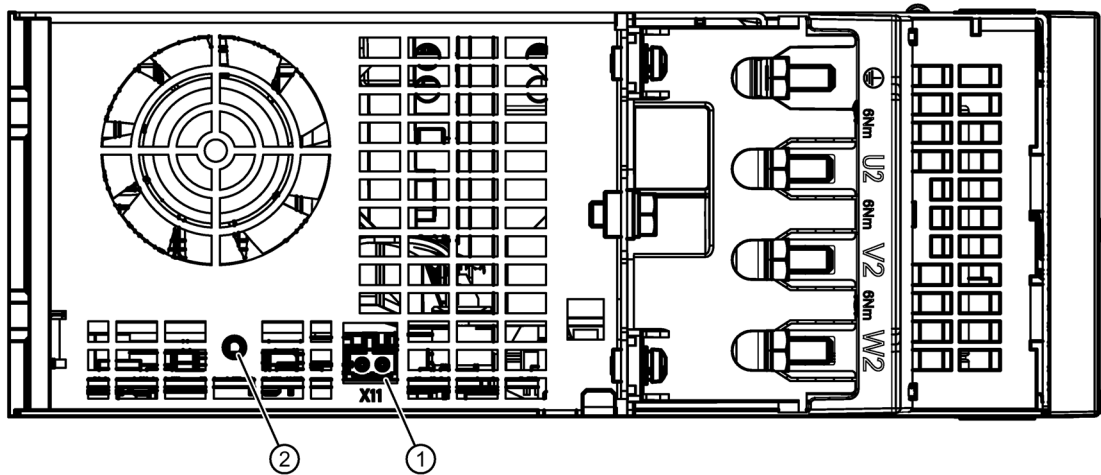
Schnittstellenübersicht Motor Module Booksize C-Type 45 A / 60 A
